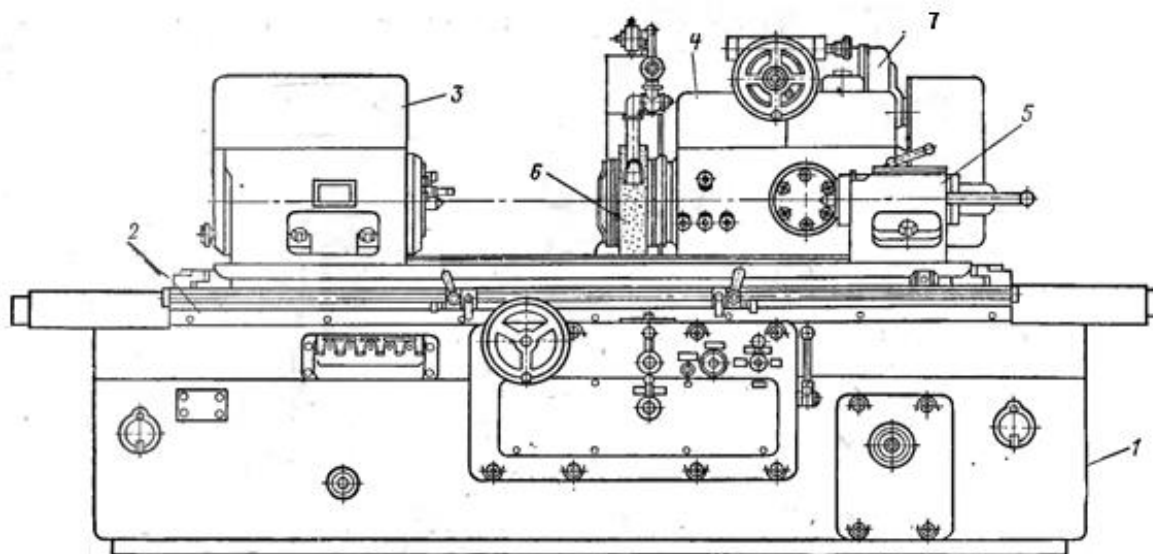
Общий вид круглошлифовального станка модели 3151
